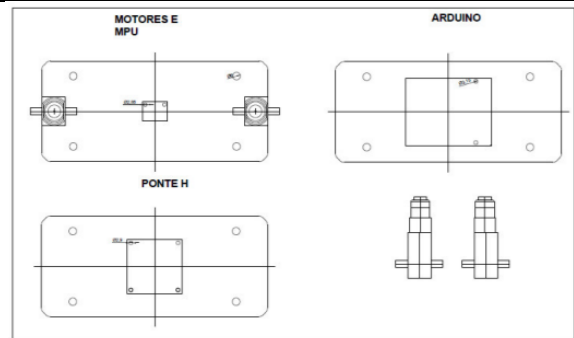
Desenho AUTOCAD. (Fonte: O autor)
